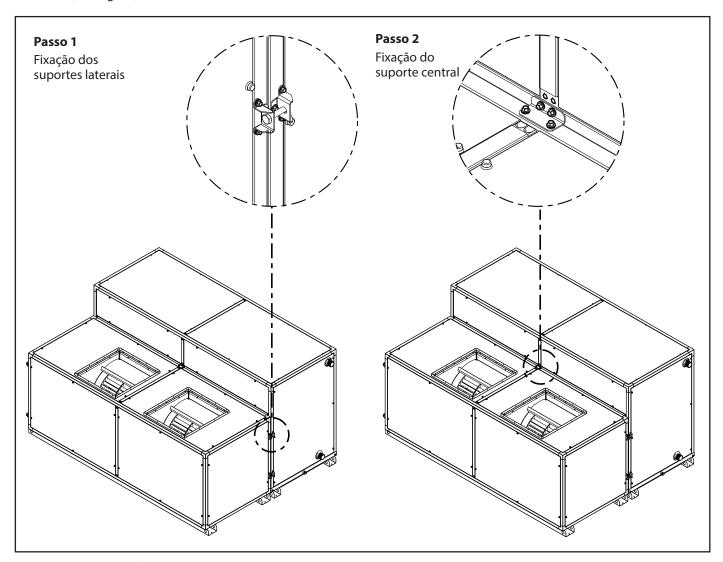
Detalhe de fixação dos módulos para montagem horizontal
